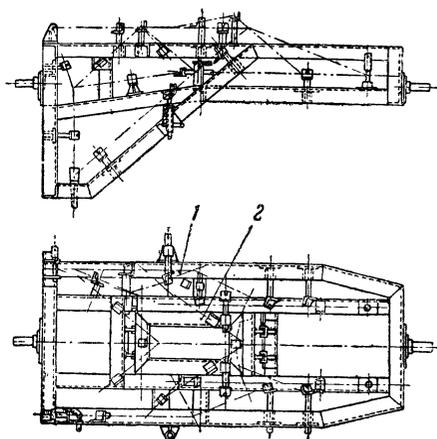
Стапель для сварки ушков под качалки.
